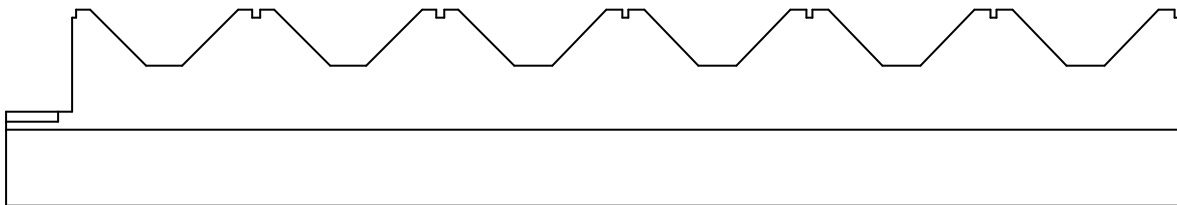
Corte del cilindro que muestra la disposición de las mordazas.
